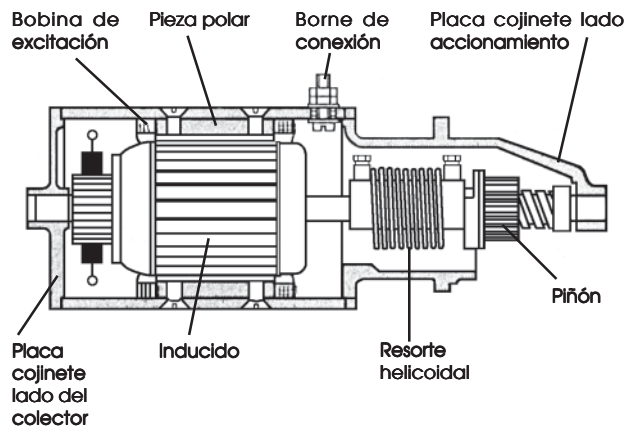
Arrancador de piñón libre y movimiento rotatorio de engrane.
